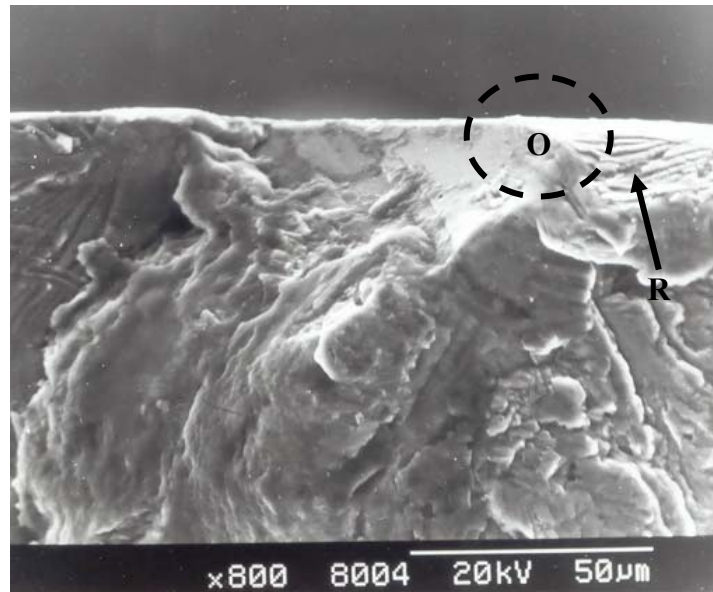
Detalle del inicio de grieta en superficie de fractura de la probeta N° 1
